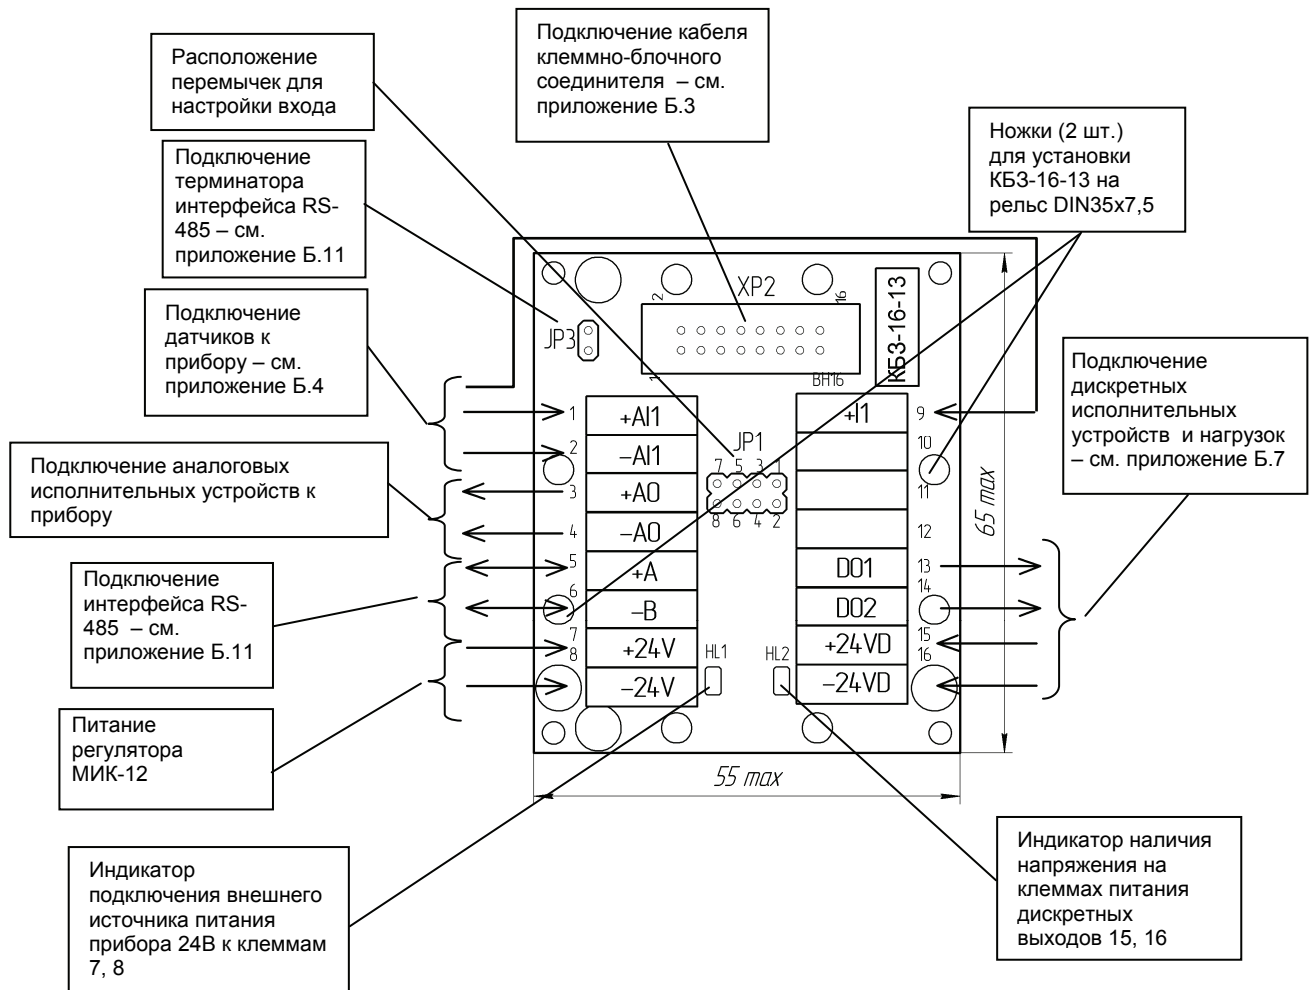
Схема расположения сигналов и габаритные размеры клеммно-блочного соединителя КБЗ-16-13
